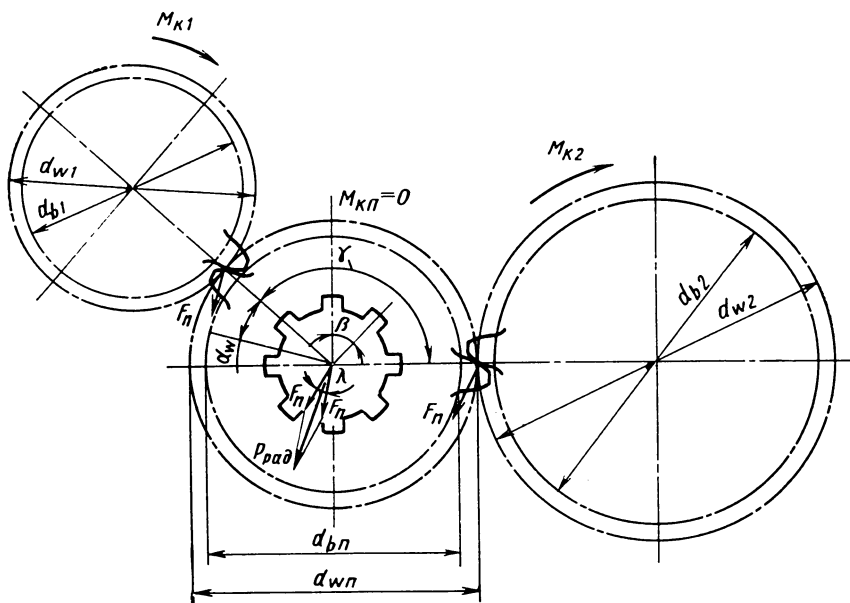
Схема шлицевого соединения вала с промежуточным зубчатым колесом
